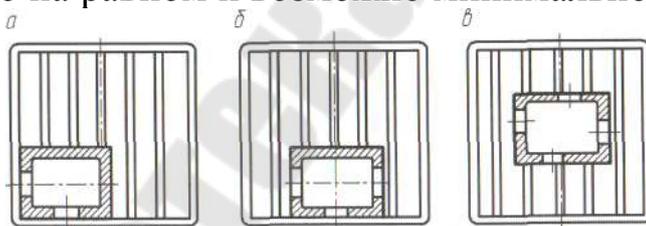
Схема расположения заготовки при обработке: а – с двух сторон; б – с трех сторон; в – с четырех сторон
